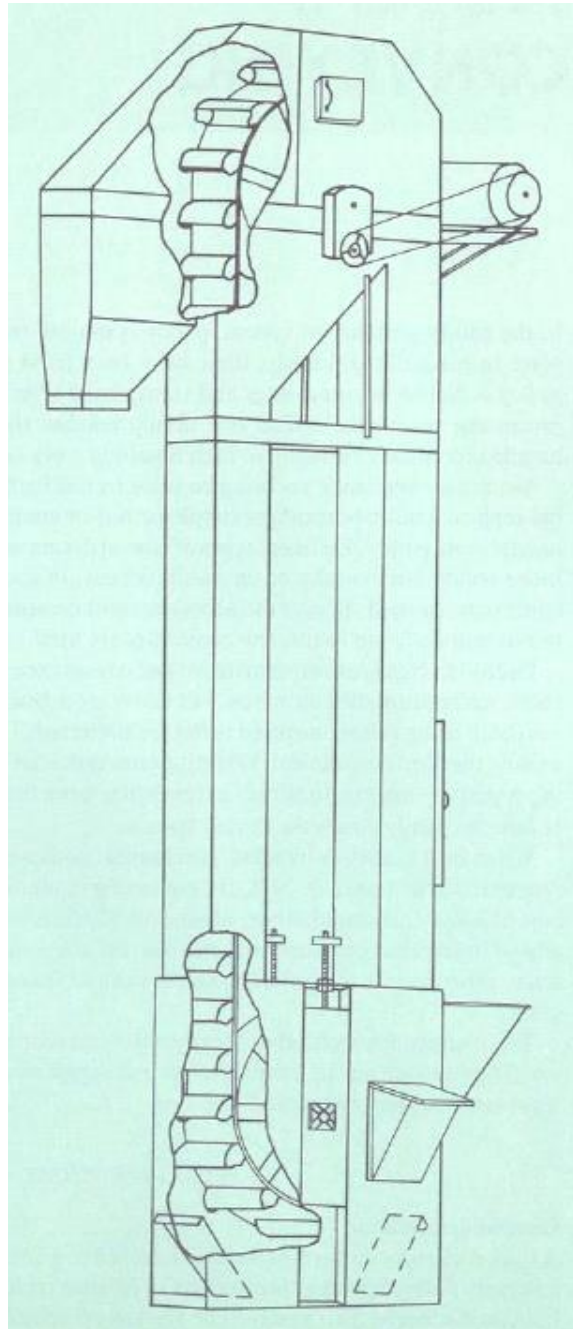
Detalle de un elevador de cangilones (Fuente: J. E. Wimberly, 1983 [44]).
